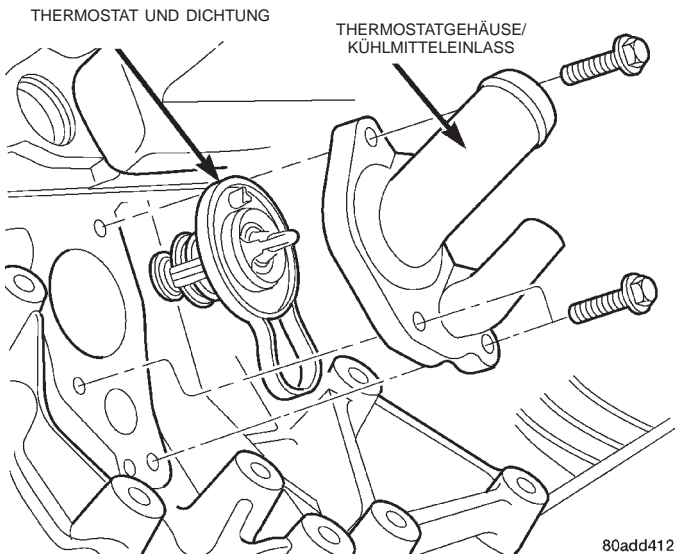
Thermostat und Gehäuse—2.7L-Motor
